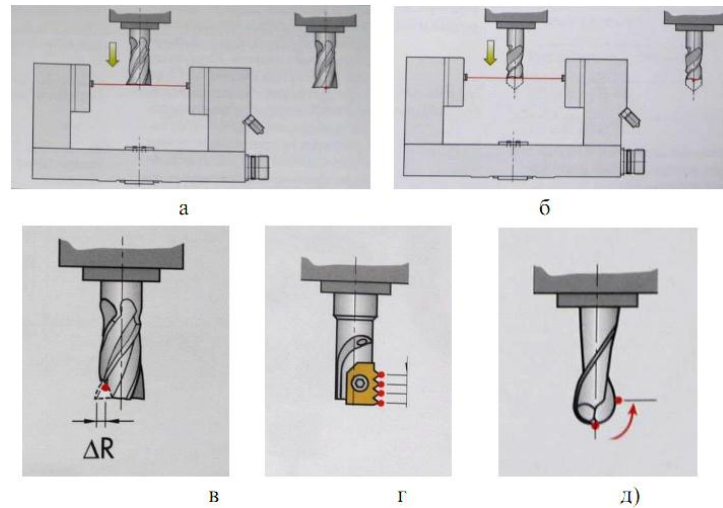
Безконтактний метод вимірювання лазерною системою TL: а – вимірювання довжини інструменту; б – розпізнавання поломки; в - вимірювання радіусу інструменту та розпізнавання пошкоджених зубів; г- контроль окремих зубів; д - контроль форми зубів
